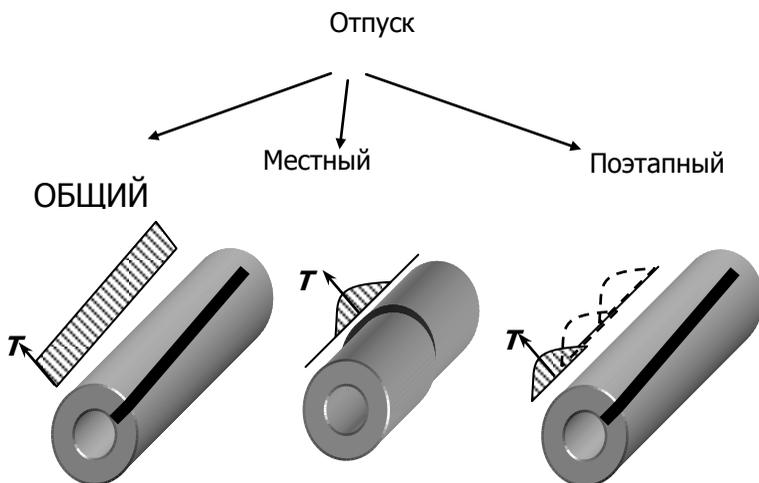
Схемы нагрева сварных конструкций при термической обработке с целью уменьшения остаточных напряжений
